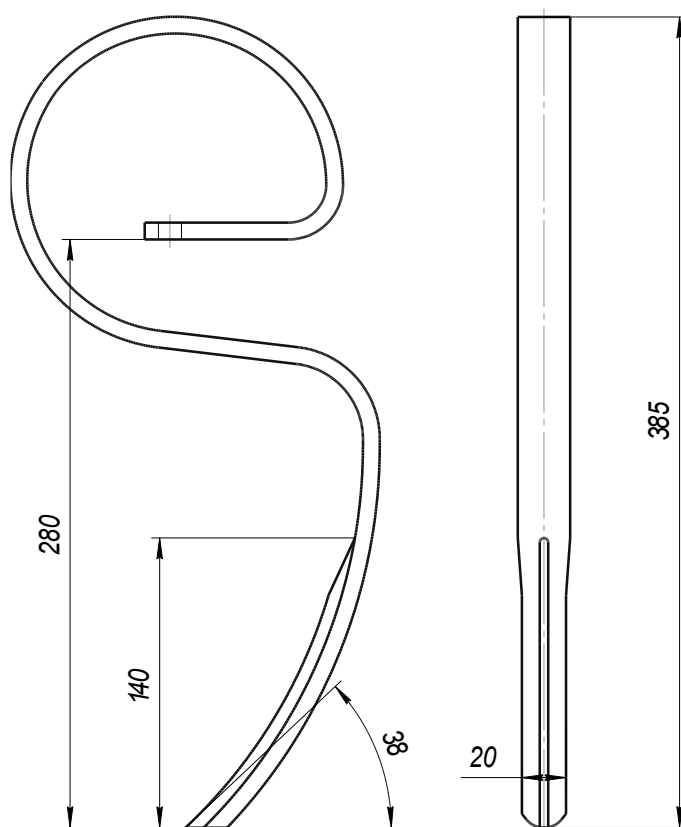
Загальний вигляд пружного зуба борінчатої культивуючої секції
